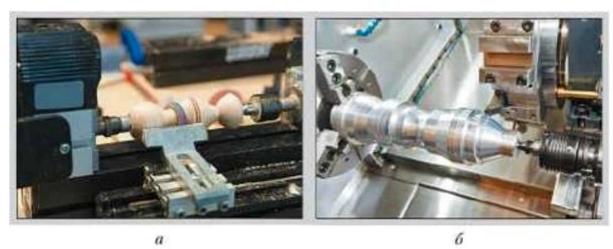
Токарная обработка материала на станке с ЧПУ: а — древесины; б — металла
